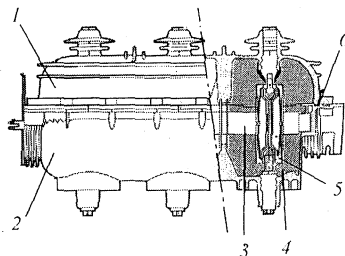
Устройство выключателя нагрузки (разъединителя): 1 — крышка; 2 — корпус; 3 — вал привода; 4 — неподвижный контакт; 5 — подвижный контакт; 6 — уплотнение
